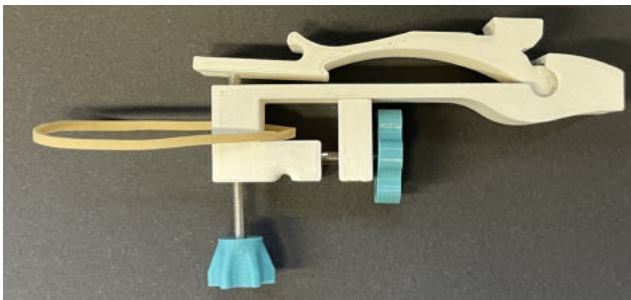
Die längere Schraube wird am Rumpf befestigt.
